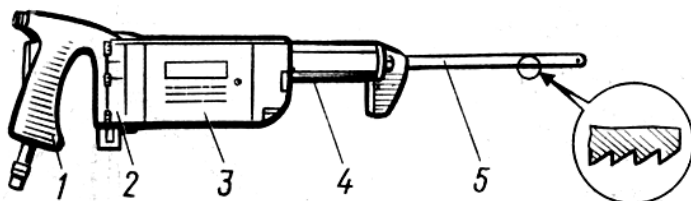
Пневматическая ручная пила: 1 – пусковое устройство; 2 – дросселирующее устройство; 3 – корпус; 4 – привод; 5 – ножовочное полотно
